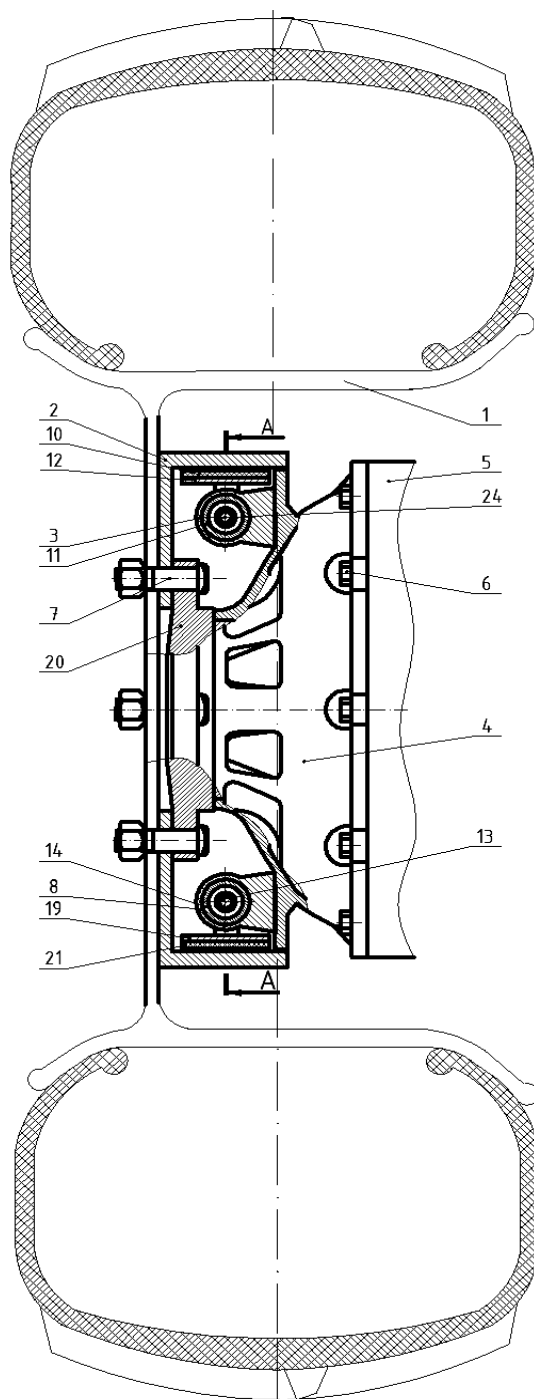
Тормоз ведущего переднего моста колесного трактора с двумя первичными тормозными колодками: 1 – колесо; 2 – тормозной барабан; 3 – корпус; 4 – тормозной шит; 5 – корпус редуктора; 6 – болт; 7 – болт; 8 – корпус; 10 – фрикционная накладка; 11 – гидроцилиндр; 12 – тормозная колодка; 13 – винт регулировочный; 14 – гидроцилиндр; 19 – тормозная колодка; 20 – полуось; 21 – фрикционная накладка; 24 – винт регулировочный [5]
